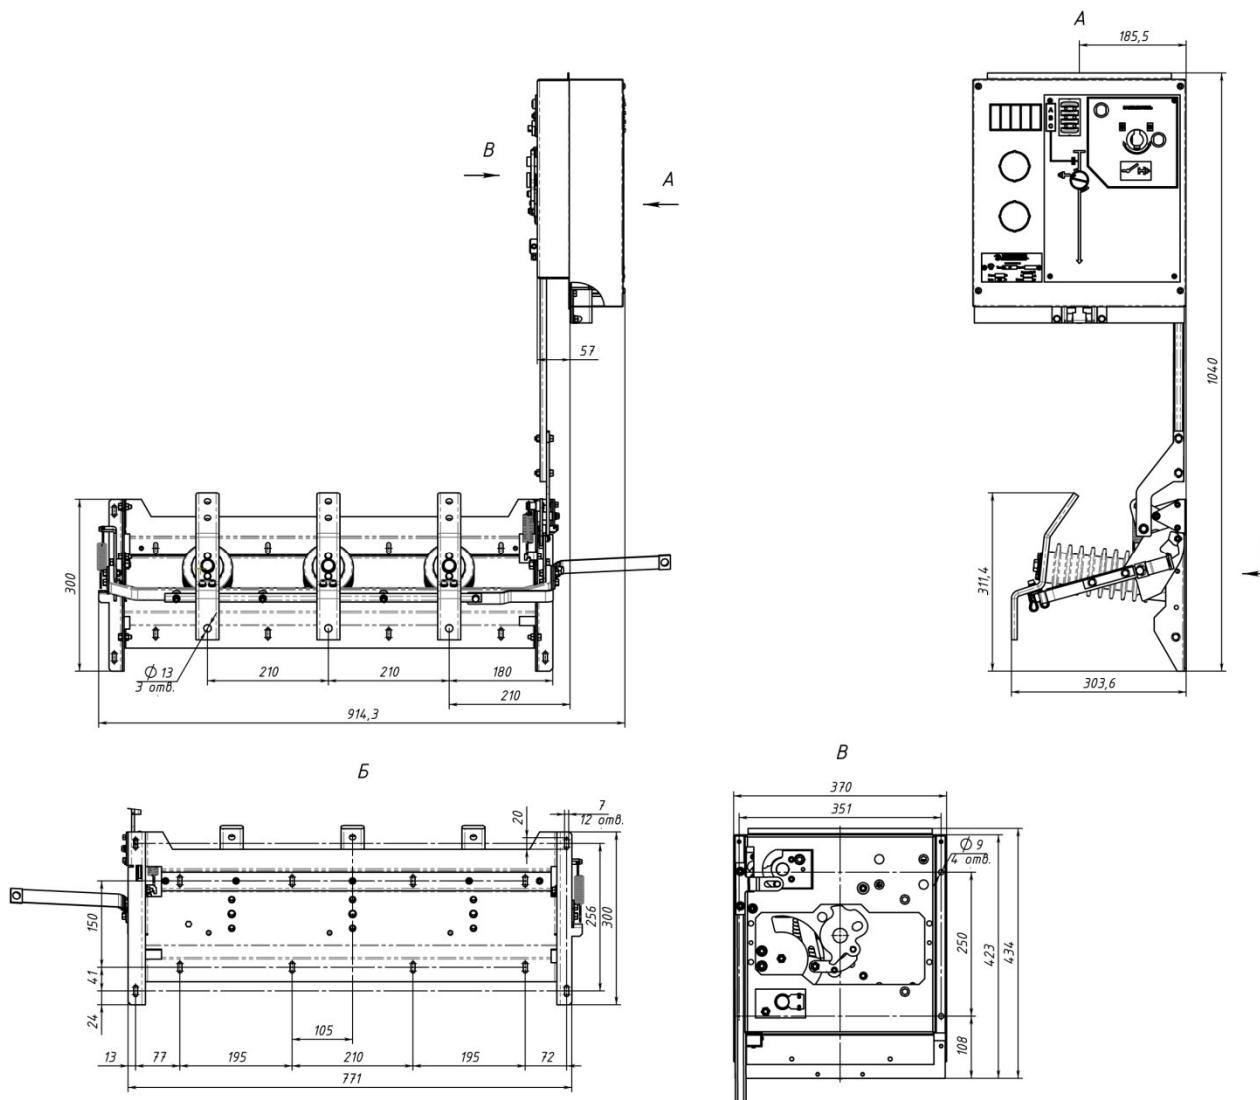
Габаритно-присоединительные размеры аппарата типов SL24-EH(A, B)
